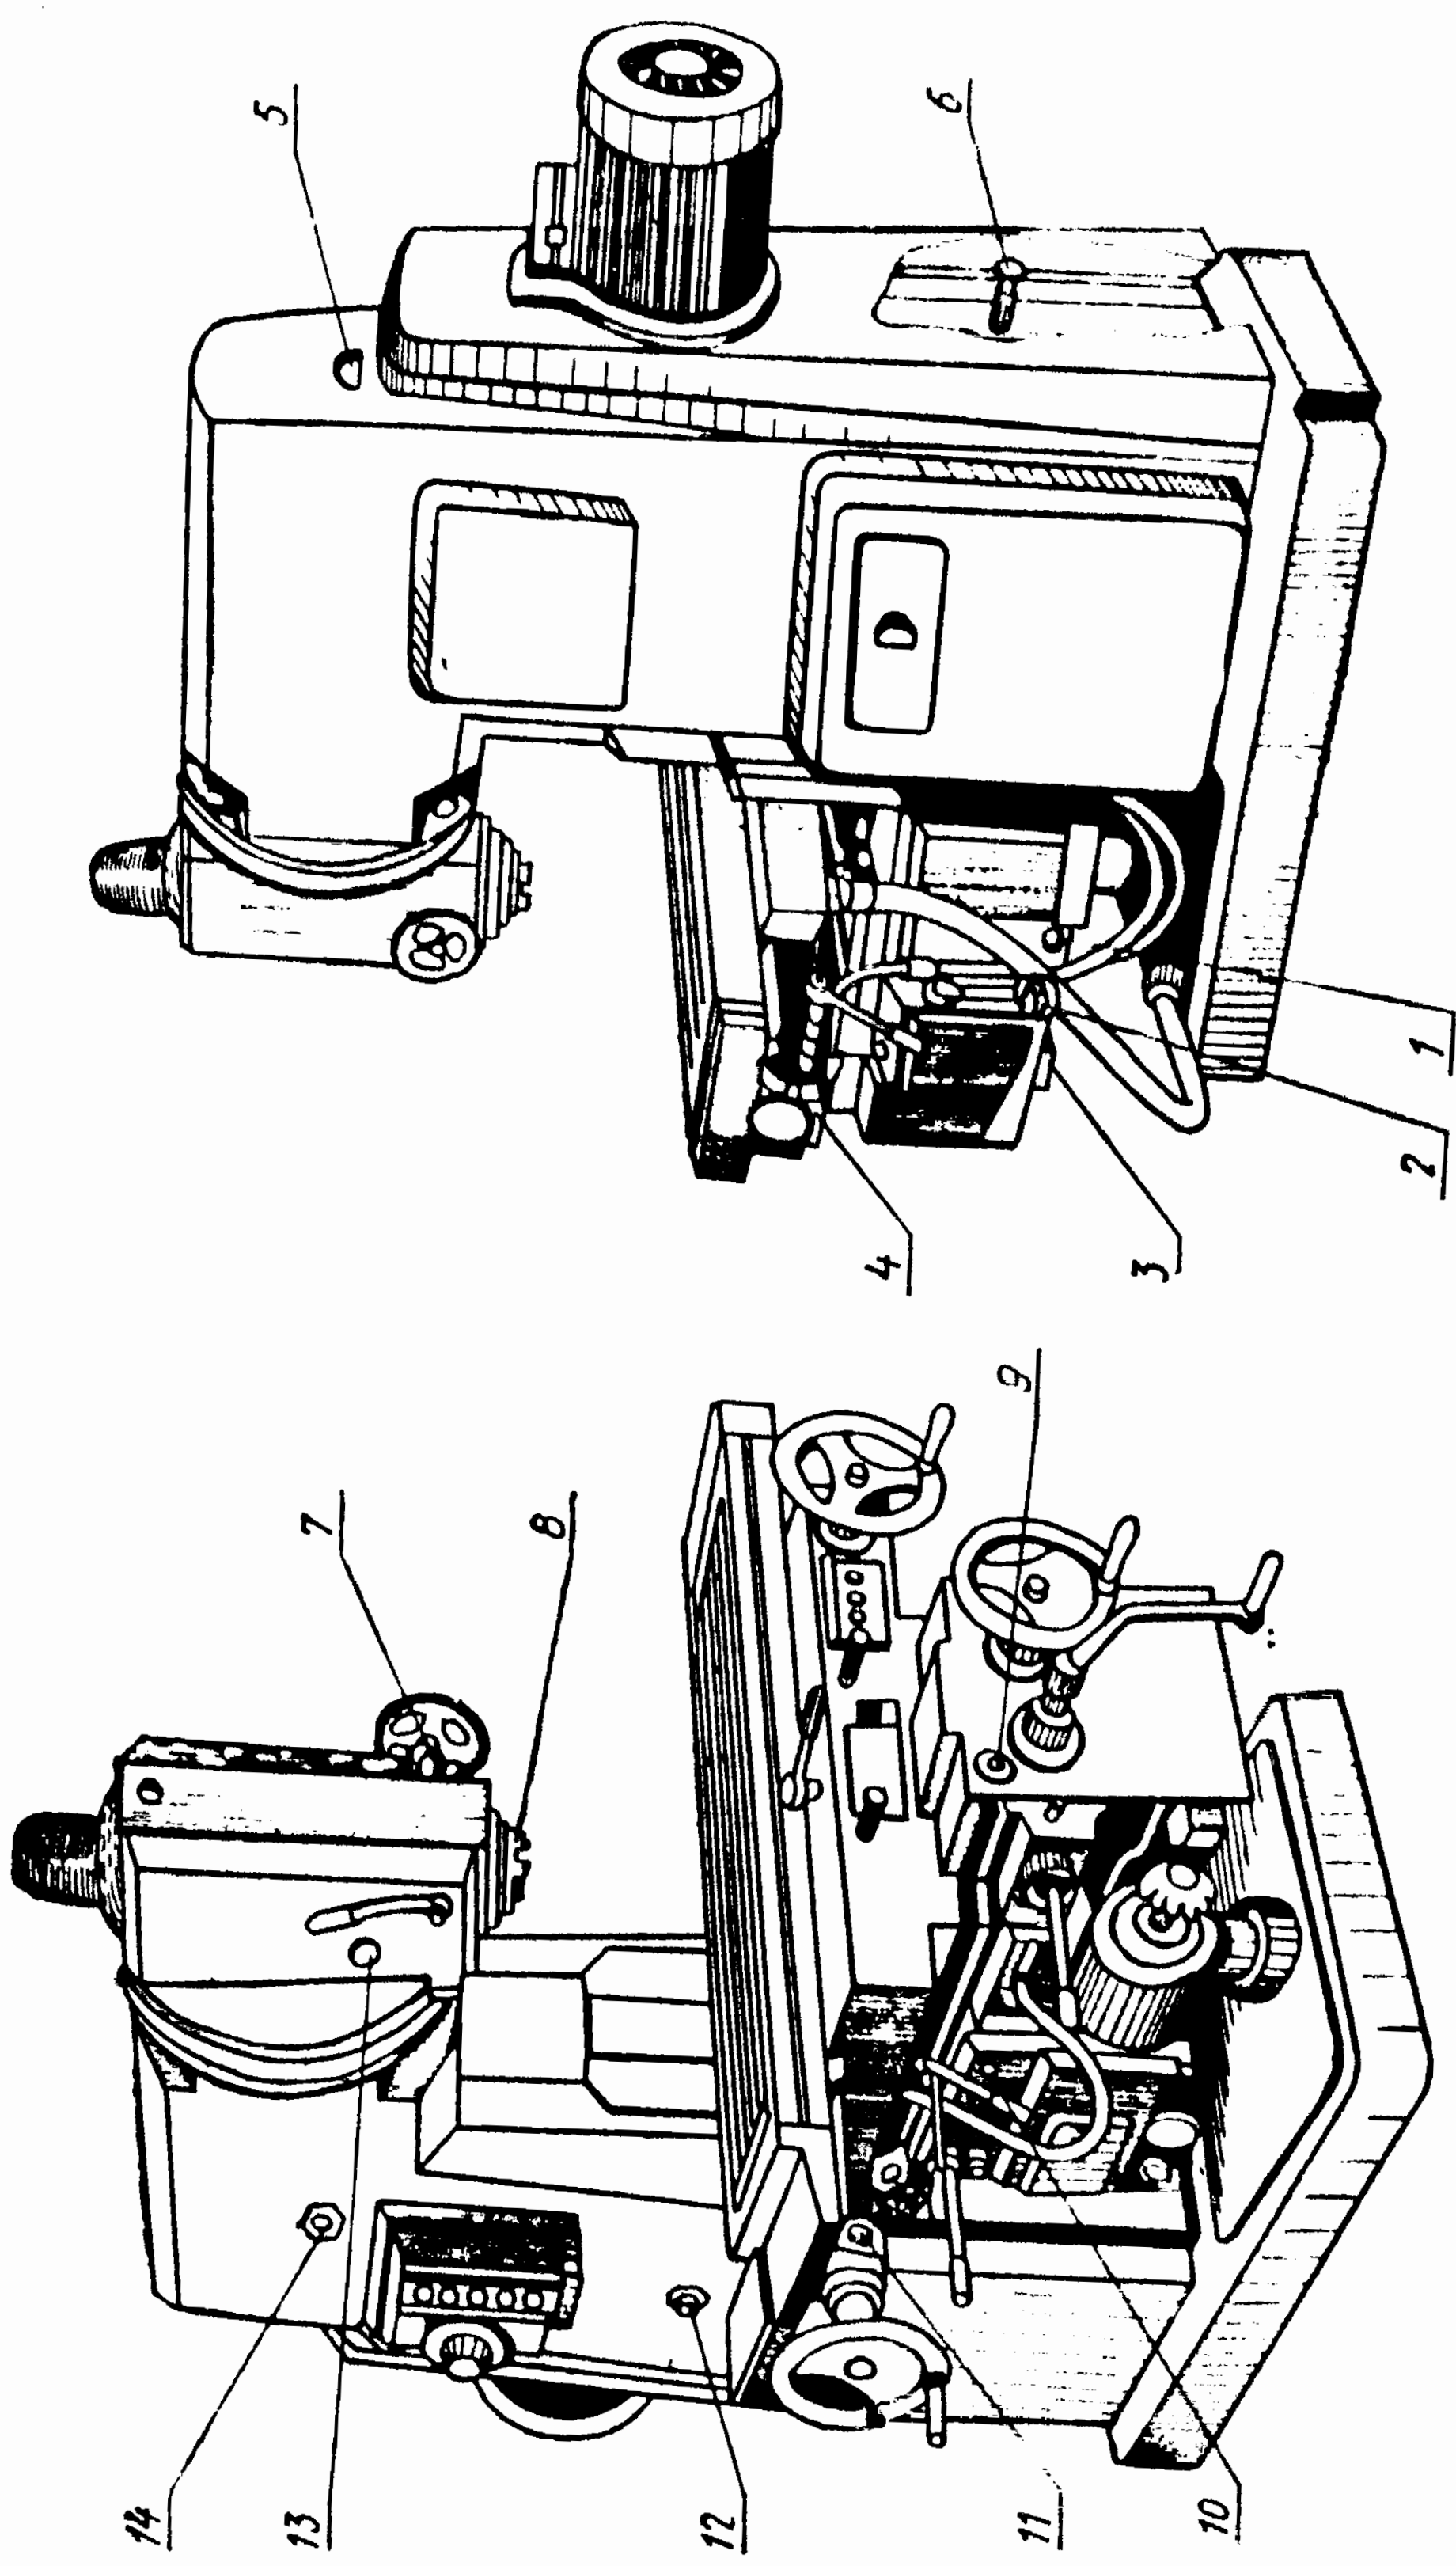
Точки смазки консольно-фрезерных станков моделей 6Р12 и 6Р13 1—14.
